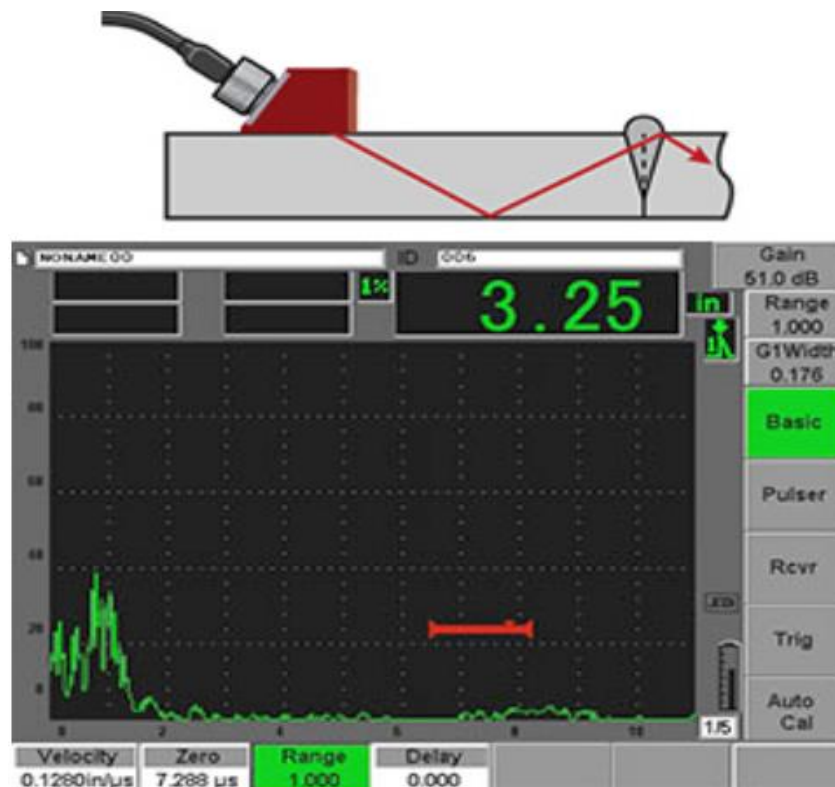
Inspección en UT de cordón de soldadura sin defectos
